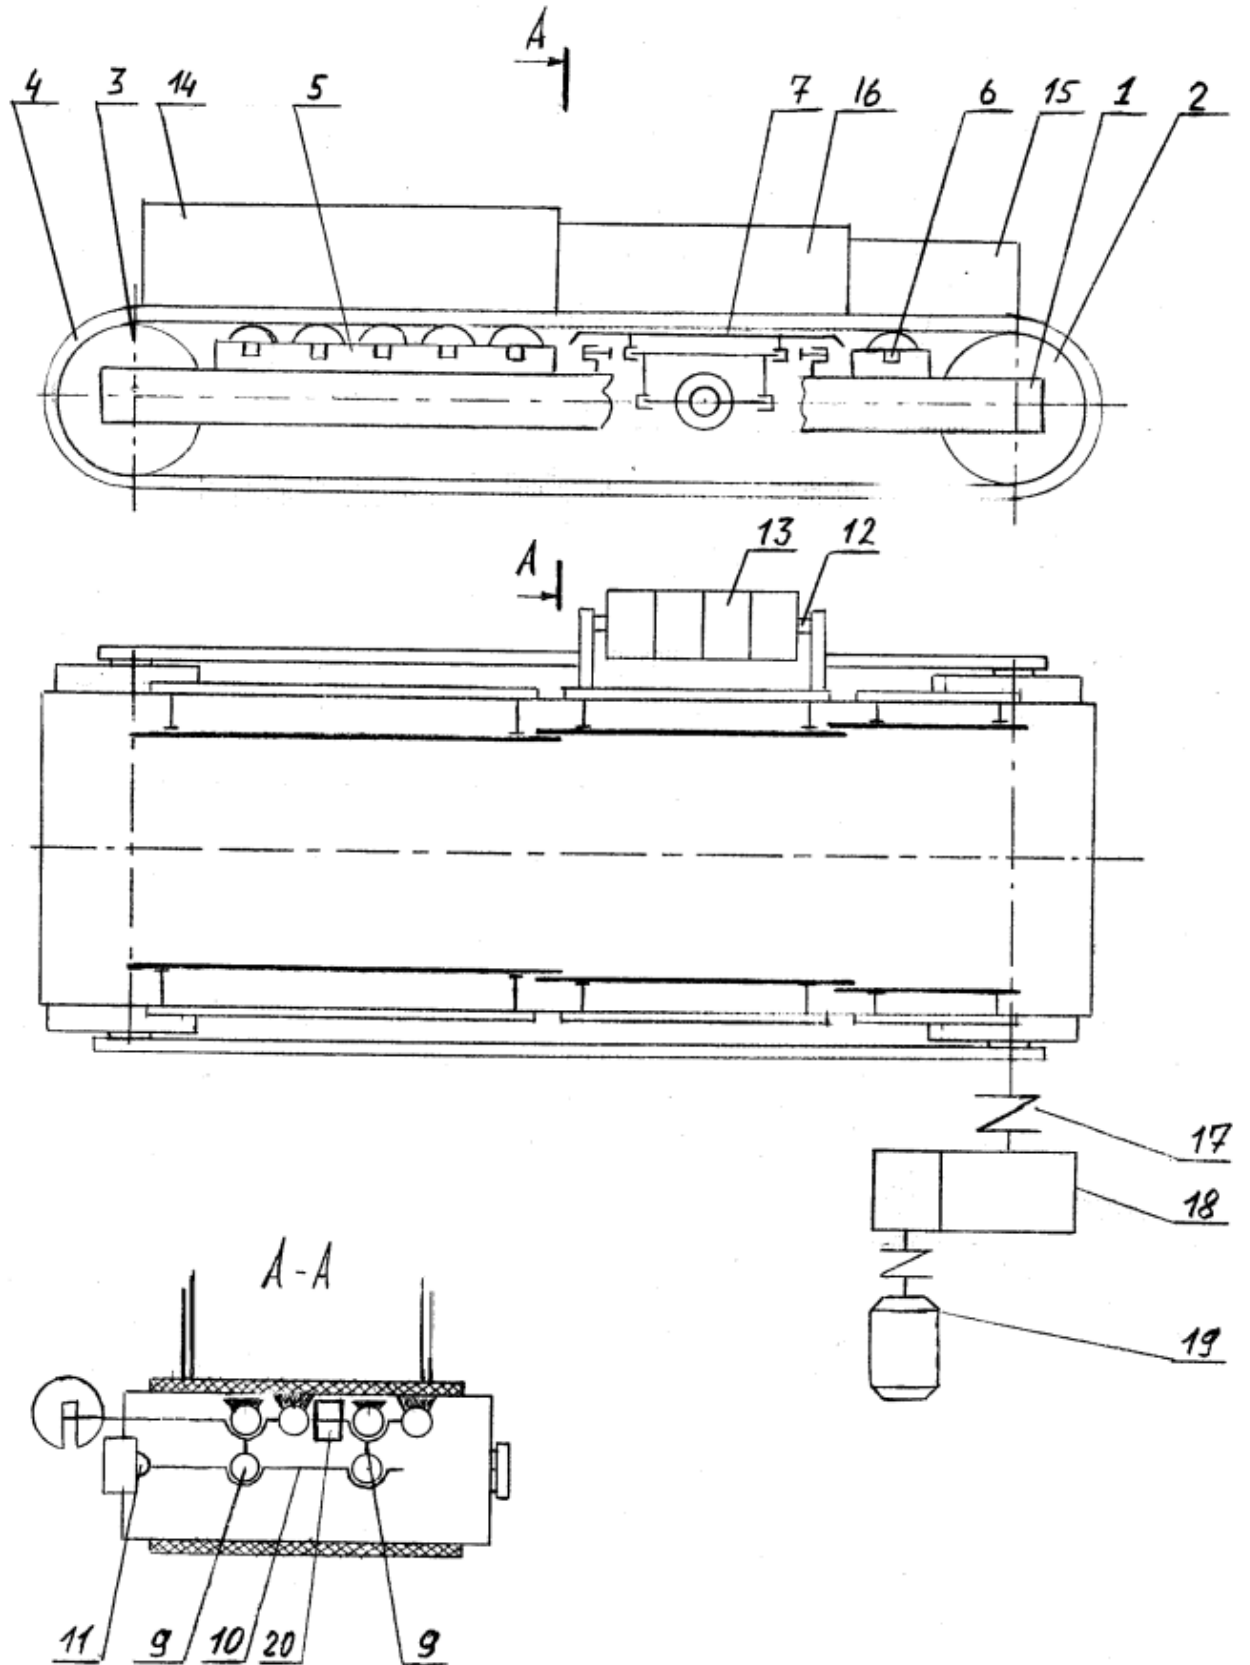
Устройство и внешний вид ленточного весодозатора
